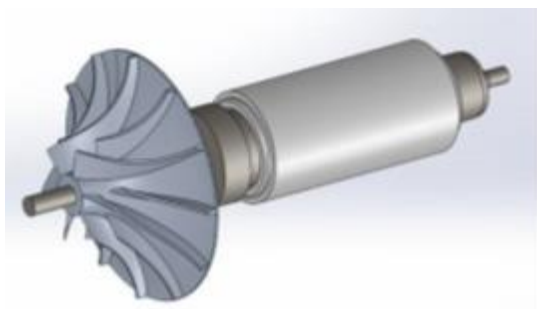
Rotrex-kompressor til DryF-projektet (SINTEF).
